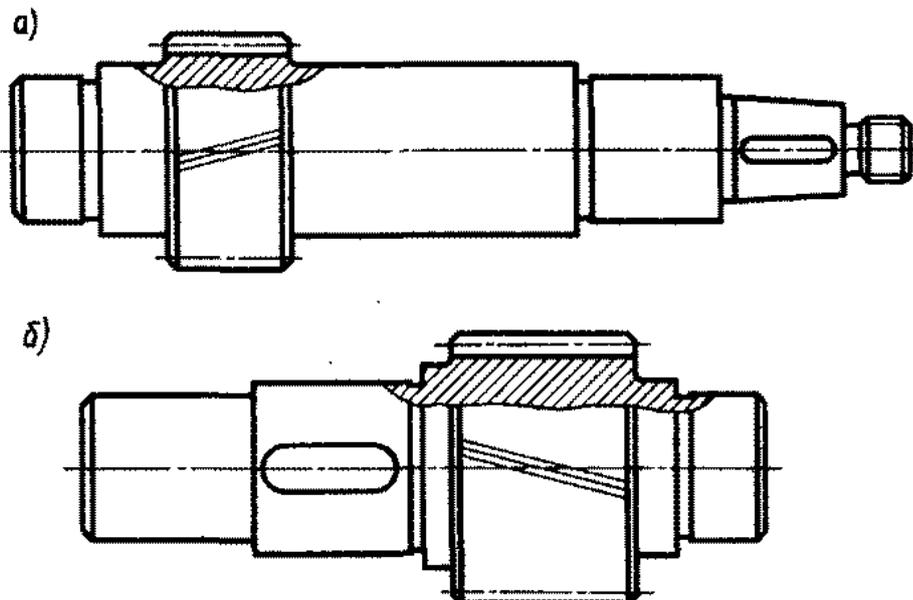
Конструкции вала-шестерни: *а*—быстроходной (с небольшим передаточным числом) и *б*— тихоходной (промежуточный вал) ступеней двухступенчатого редуктора
